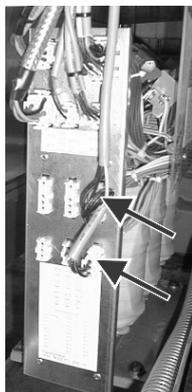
Transformateur T1 à la paroi arrière de la machine à tricoter
